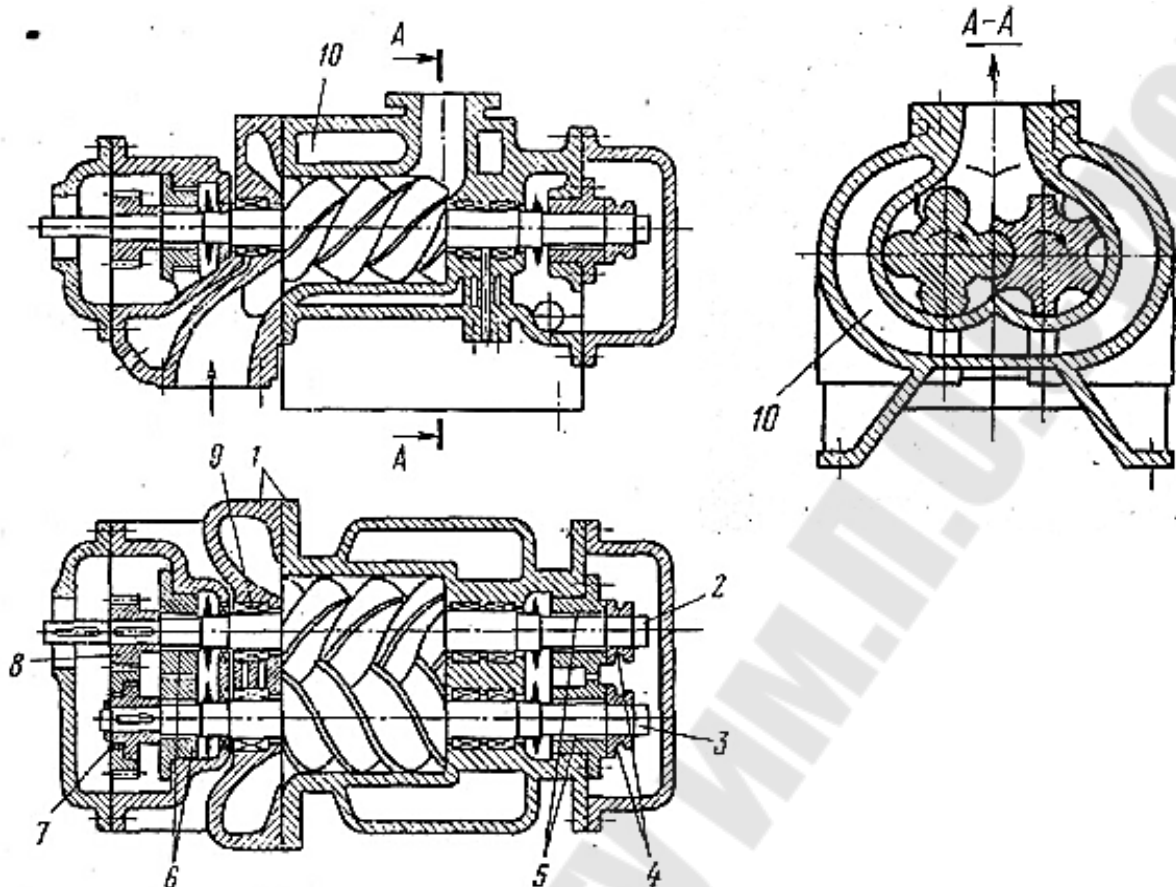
Винтовой компрессор с охлаждаемым корпусом:
